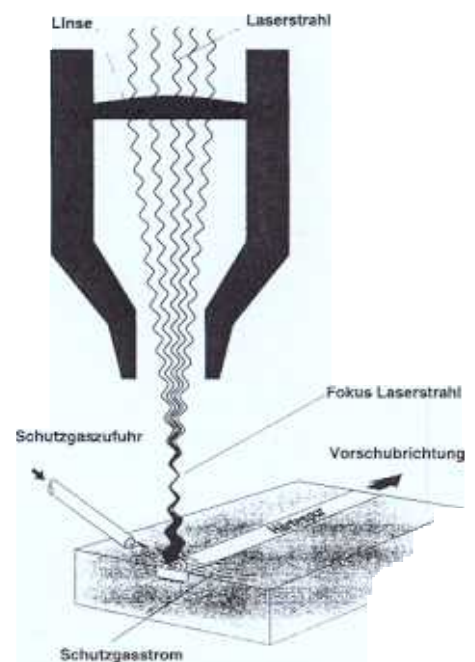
Prinzipbild Laserstrahl-Oberflächenbearbeitung
